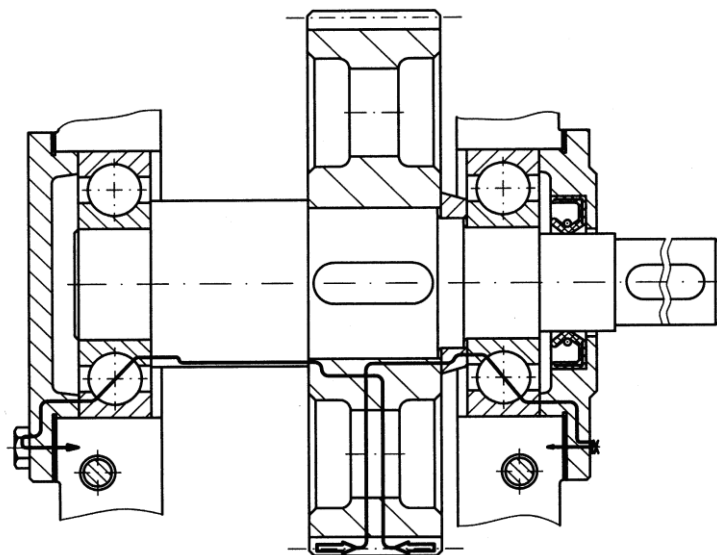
Montaj cu fixare axială la ambele capete, cu rulmenți radiali cu bile, montaj în "X"
